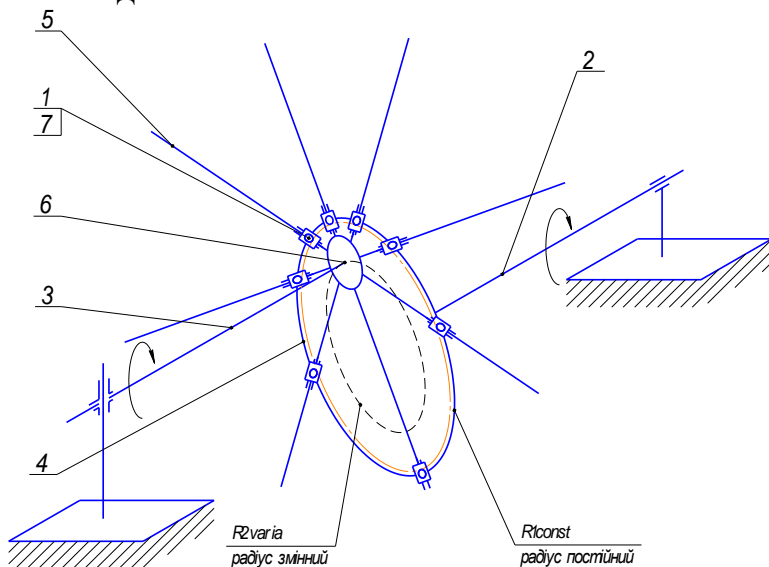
Кінематична схема варіатора: 1-механізм вільного ходу; 2-ведучий вал; 3-ведений вал; 4-диск; 5-спиця; 6-маточина; 7-повзун
